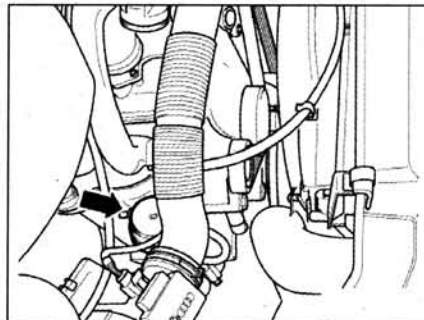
Расположение масляного фильтра двигателя AGX.
